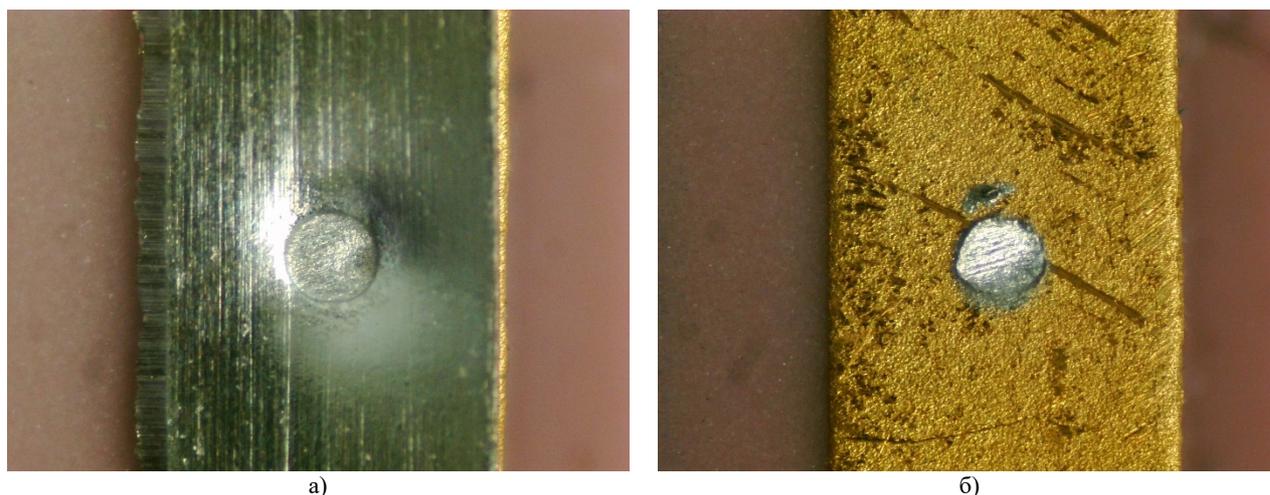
Фрагмент ободка основания корпуса с закрепленной преформой (а) и после ее отрыва(б)
